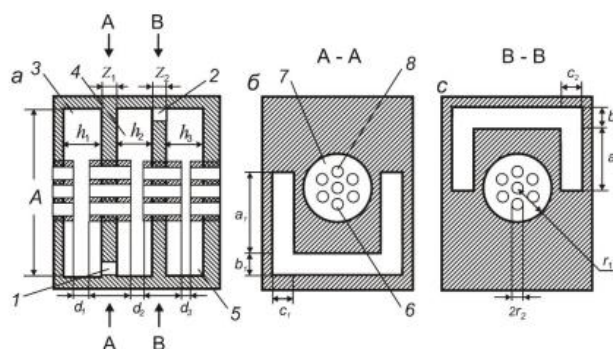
Схематическое изображение трехзворного резонатора:
